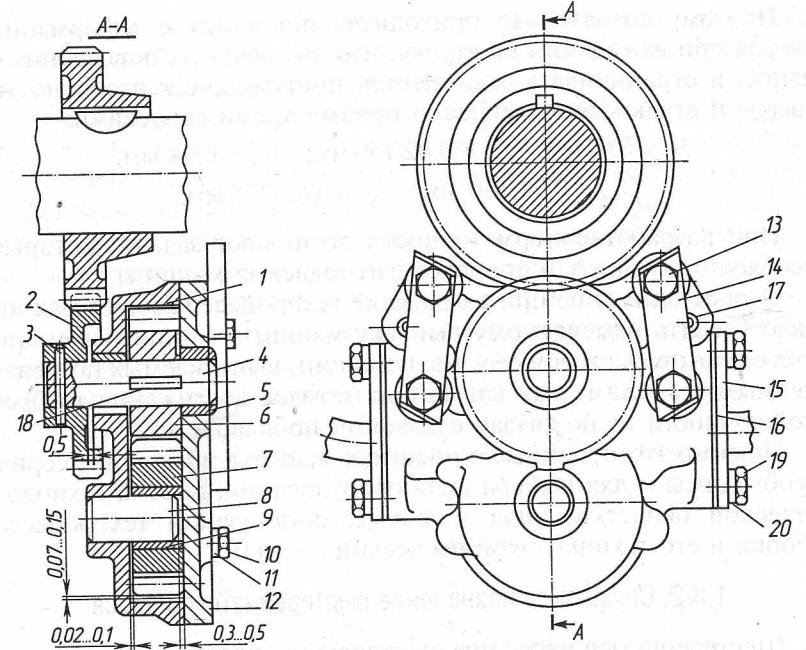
Общий вид шестеренчатого насоса трактора: 1 — корпус; 2 — ведомое зубчатое колесо; 3, 17 — штифт; 4 — валик; 5, 9 — втулка; 6, 7 — зубчатое колесо; 8 — ось; 10, 19 — винт; 11, 20 — шайба; 12 — крышка; 13 — болт; 14 — стопорная пластина; 15 — труба приемника; 16 — прокладка; 18 — шпонка
